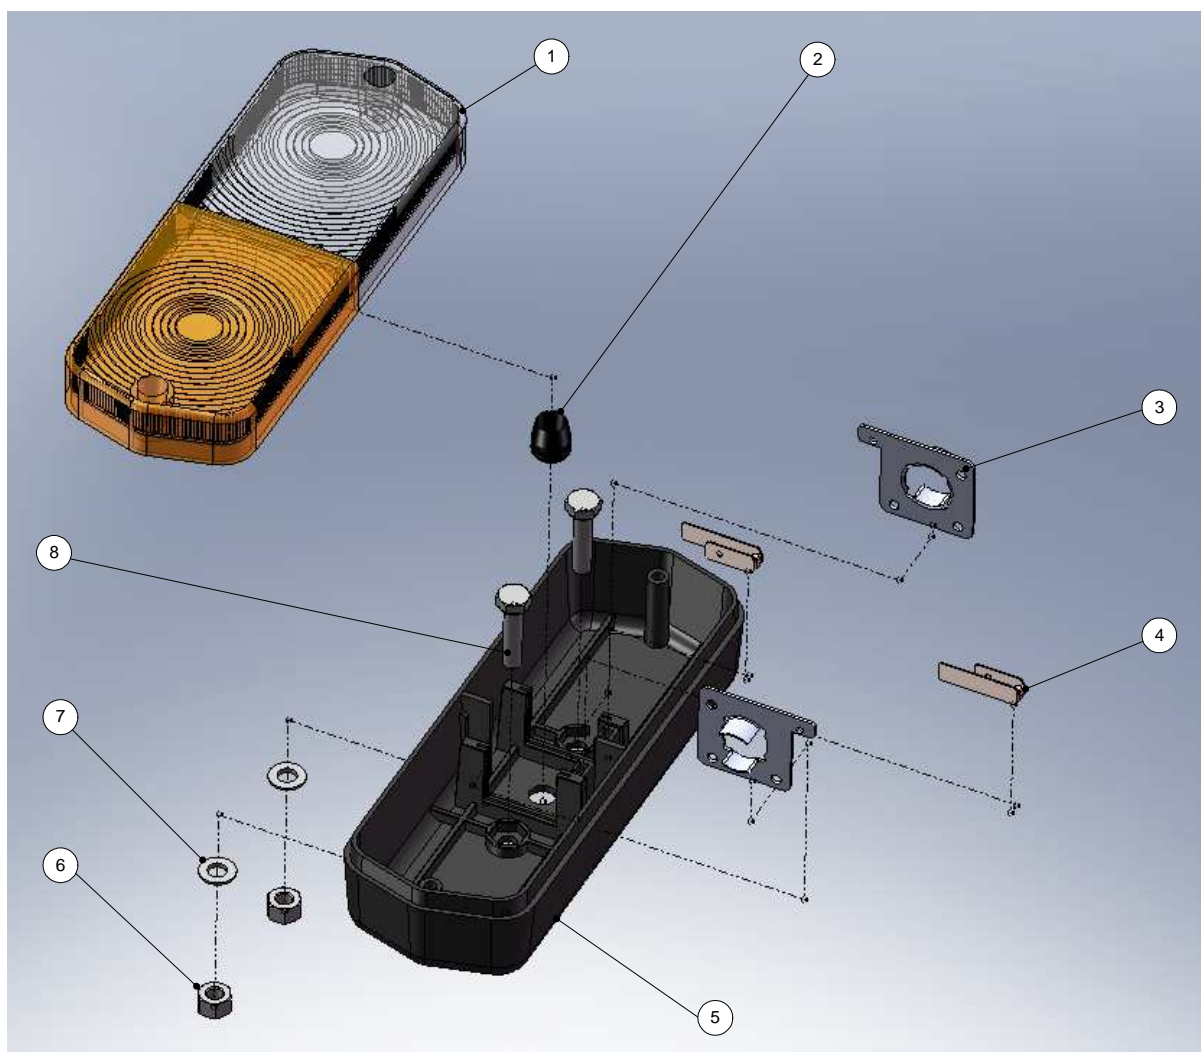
Vista Explodida do Farolim "Valmet" Modificado
